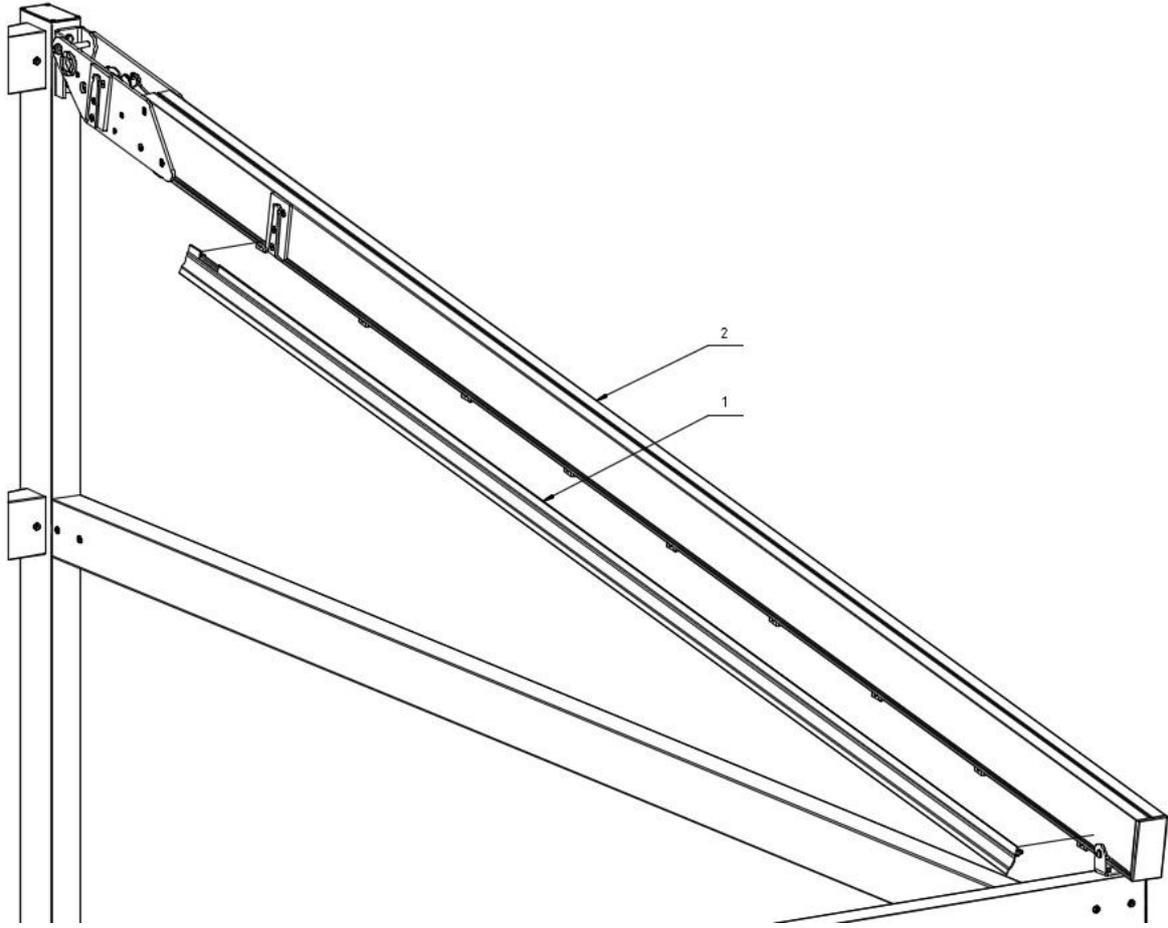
Montage de joint du module mobile: 1 – Joint du module mobile, 2 – Poutre de guidage
